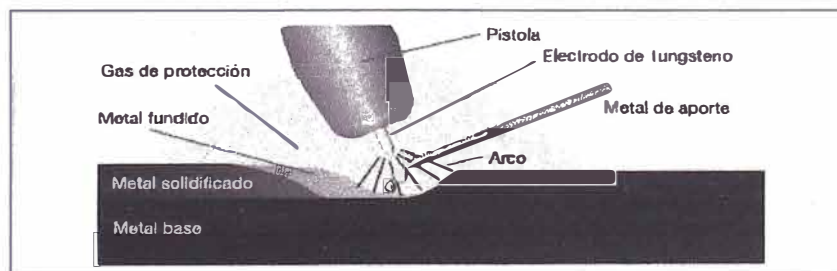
Esquema Proceso GTAW (Fuente: Manual de Soldadura Indura)
